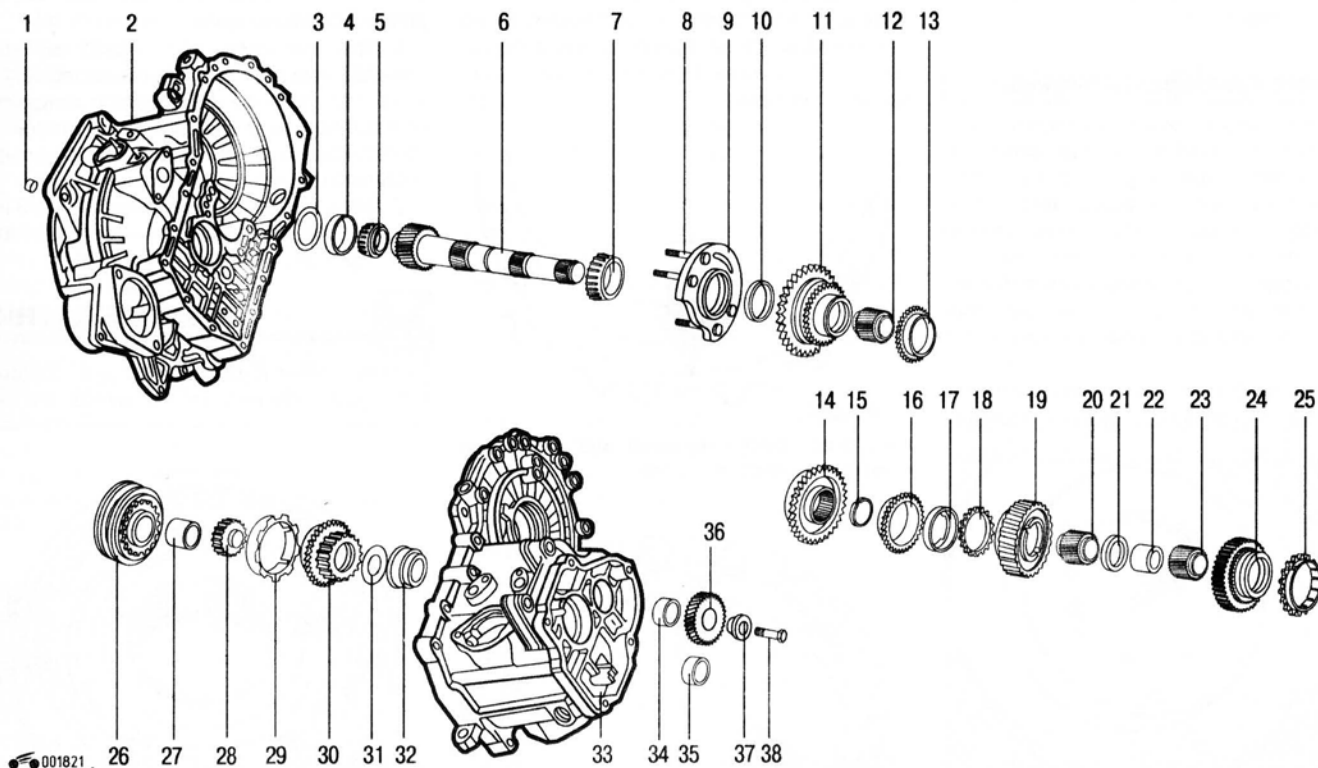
Вторичный вал и его детали: 1 — гайка; 2 — картер сцепления; 3 — шайба; 4 — чашка конического подшипника; 5 — конический подшипник (малый); 6 — вторичный вал; 7 — конический подшипник (большой); 8, 38 — болты; 9 — опора подшипника; 10, 21, 31 — упорные шайбы; 11 — шестерня I передачи; 12 — игольчатый подшипник шестерни I передачи; 13 — кольцо синхронизатора I передачи; 14 — ступица синхронизатора I и II передач; 15 — стопорное кольцо; 16 — кольцо синхронизатора II передачи; 17 — внешнее кольцо; 18 — внутреннее кольцо синхронизатора; 19 — шестерня II передачи; 20 — игольчатый подшипник шестерни II передачи; 22 — втулка игольчатого подшипника; 23 — игольчатый подшипник шестерен III передачи; 24 — шестерня III передачи; 25 — кольцо синхронизатора III передачи; 26 — ступица синхронизатора III и IV передач; 27 — втулка игольчатого подшипника; 28 — игольчатый подшипник шестерни IV передачи; 29 — кольцо синхронизатора IV передачи; 30 — шестерня IV передачи; 32 — игольчатый подшипник; 33 — картер коробки передач; 34 — опорная втулка; 35, 37 — втулки; 36 — шестерня V передачи
